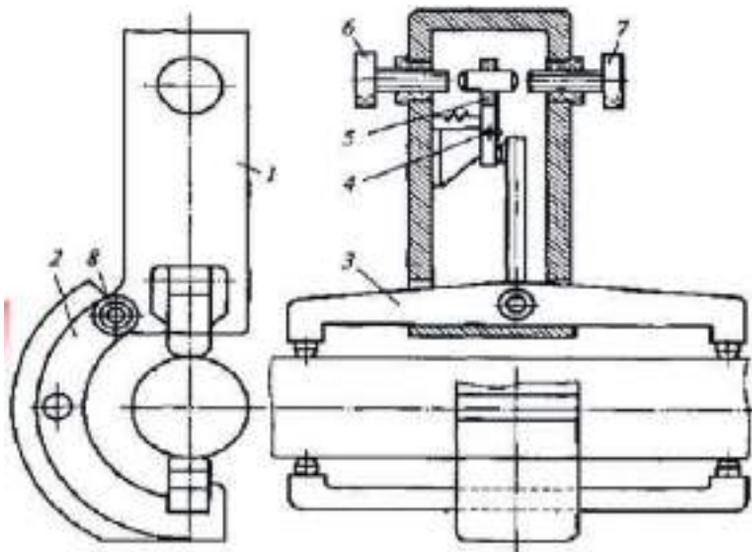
Схема автоматического контроля конусности вала устройством с двухконтактной скобой
